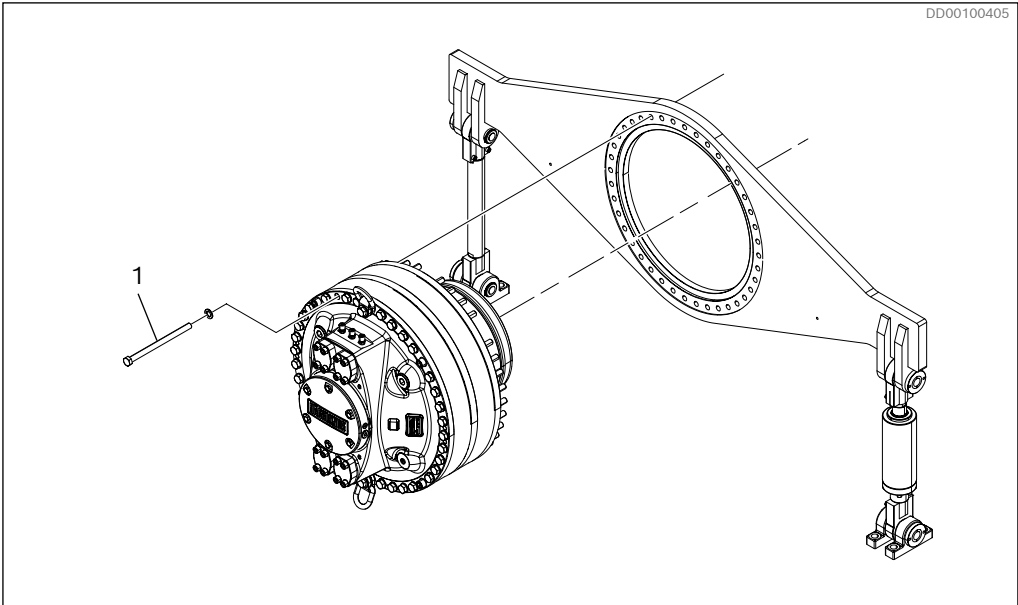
Монтаж моментного рычага с двумя плечами DTCB 0400 – DTCB 1120 для CB 280 – CB 1120
